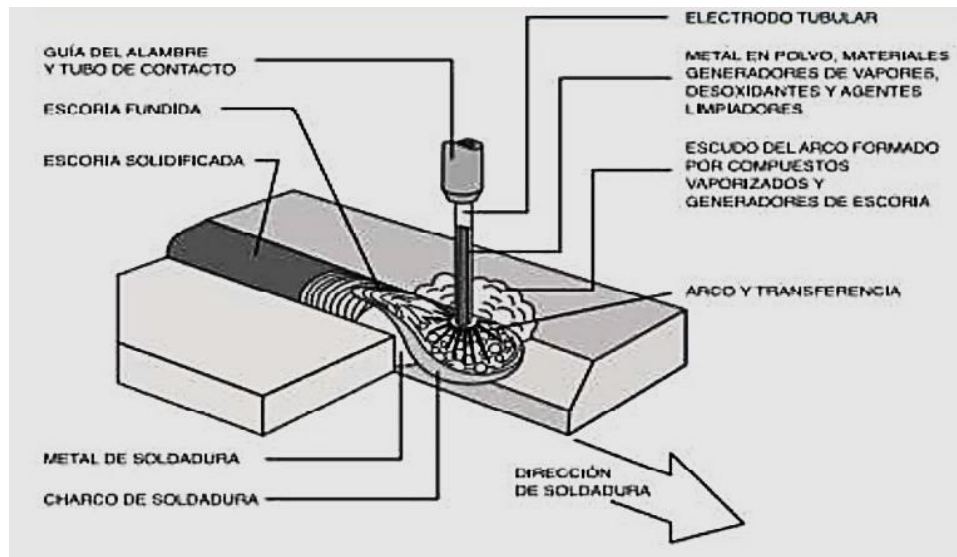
Soldadura por arco con alambre autoprotegido (FCAW-SS)
